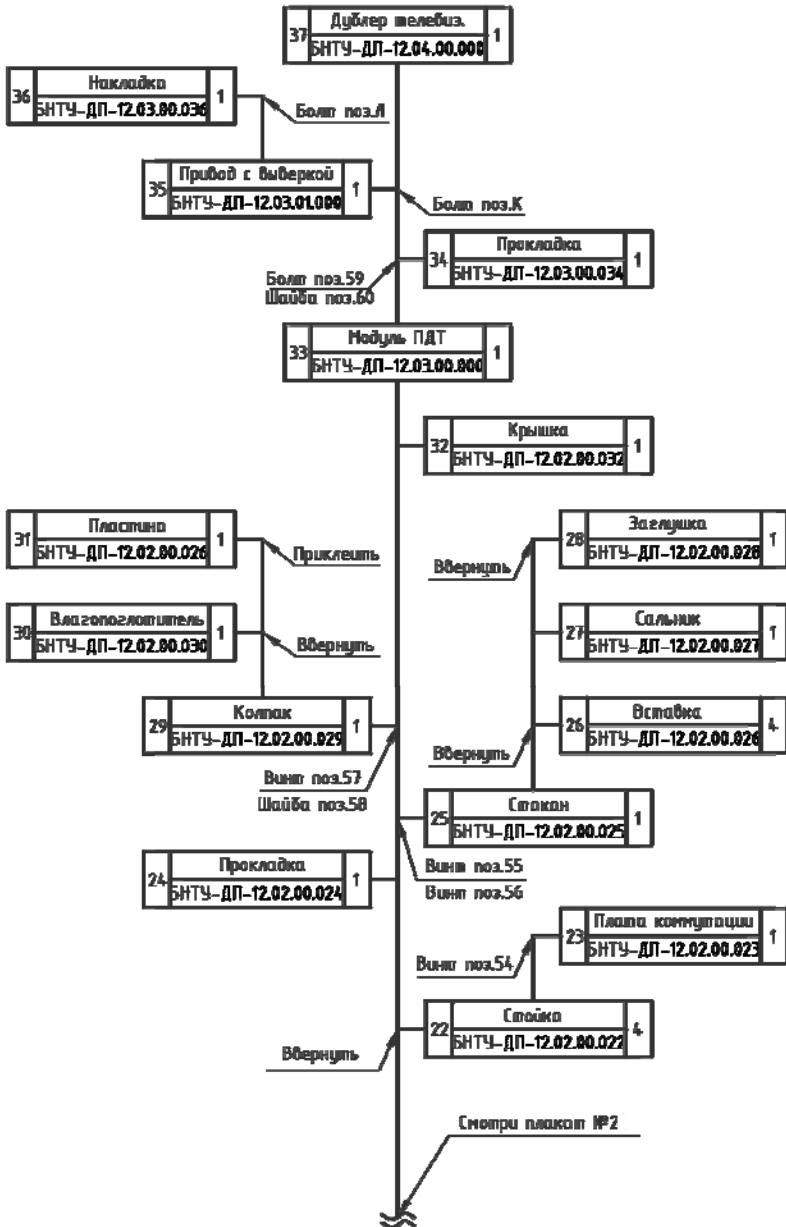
Схема сборки дублира телевизионного танкового прицеда (лист 1)
